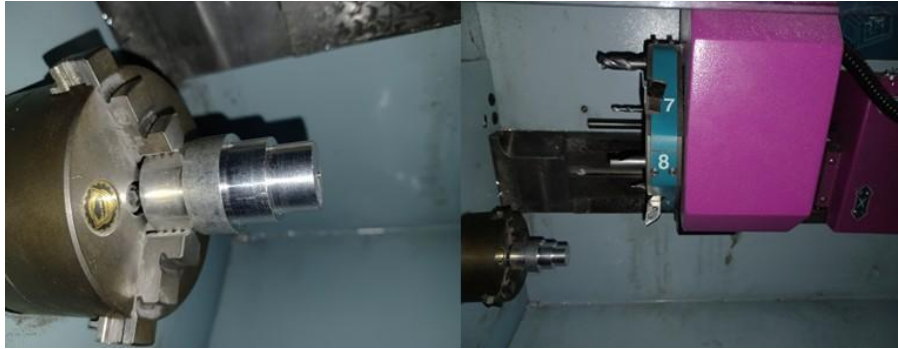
Pièce à usiner après découpe selon la méthode TPOA.
